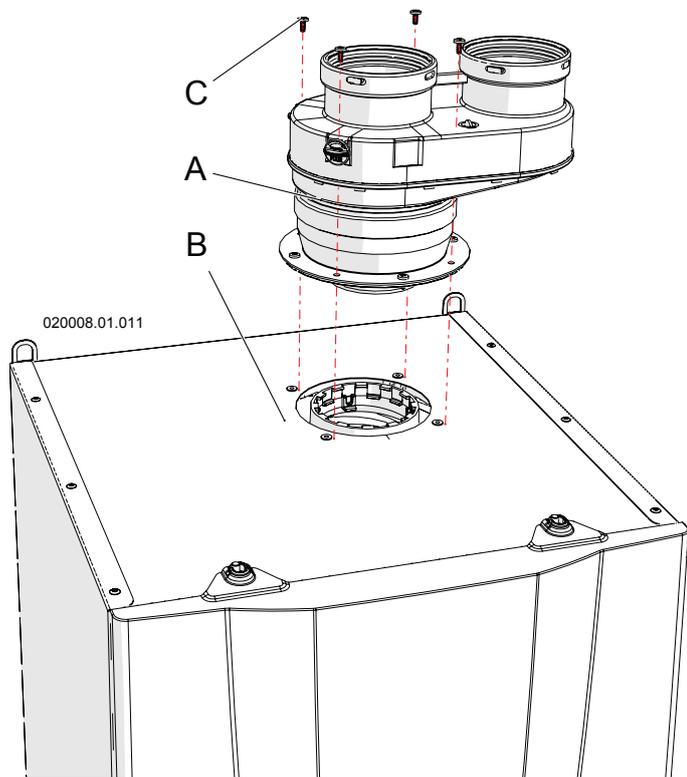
Installazione del sistema "Sdoppiato 80/80PP"
